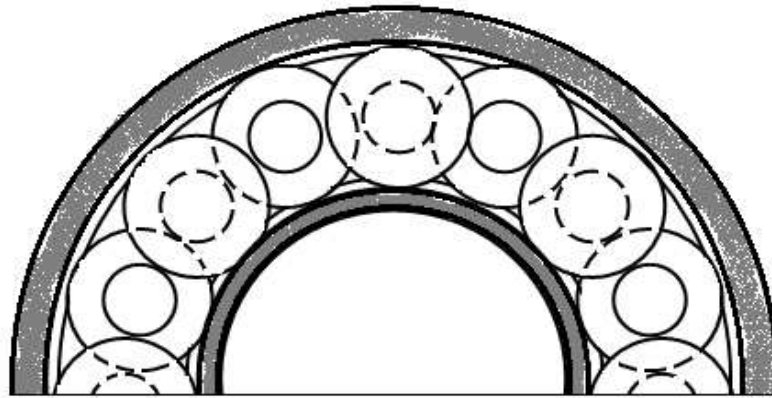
Вид половины однорядного одноярусного цилиндрического бессепараторного роликоподшипника
